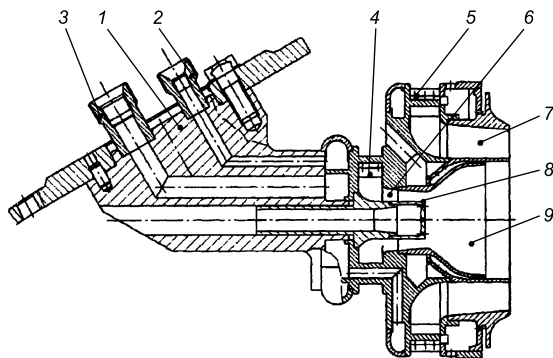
Горелочное устройство КС ГТД ДН80 [9]:
